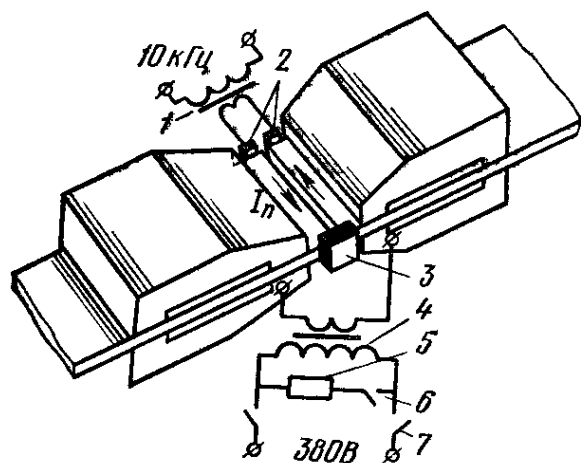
Принципиальная схема высокочастотного подогрева в машине для стыковой сварки оплавлением: 1 — высокочастотный трансформатор, 2 — контакты, 3 — переключатель, 4 — первичная обмотка сварочного трансформатора, 5 — сопротивление, 6 — управляющий контакт, 7 — сварочные контакты
